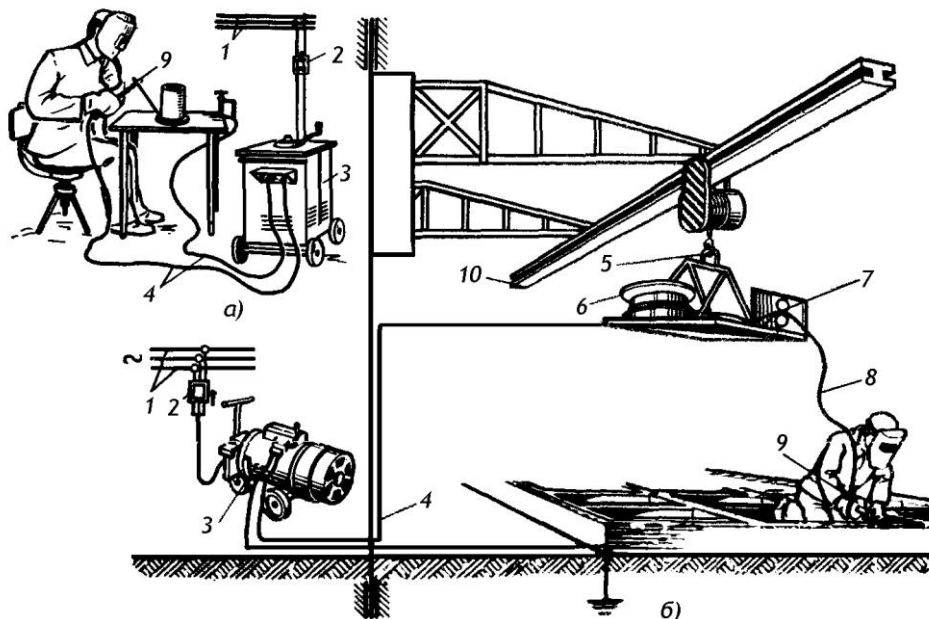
Сварочные посты для ручной и механизированной сварки, где а – ручная сварка от сварочного трансформатора или сварочного выпрямителя, б – сварка шланговым полуавтоматом; 1 – сеть электропитания, 2 – рубильник или магнитный пускатель, 3 – источник питания дуги, 4 – сварочные провода, 5 – подвеска полуавтомата, 6 – катушка с электродной проволокой, 7 – механизм подачи проволоки, 8 – шланг для подачи электродной проволоки, 9 – горелка или электрододержатель, 10 – консоли с рельсом
